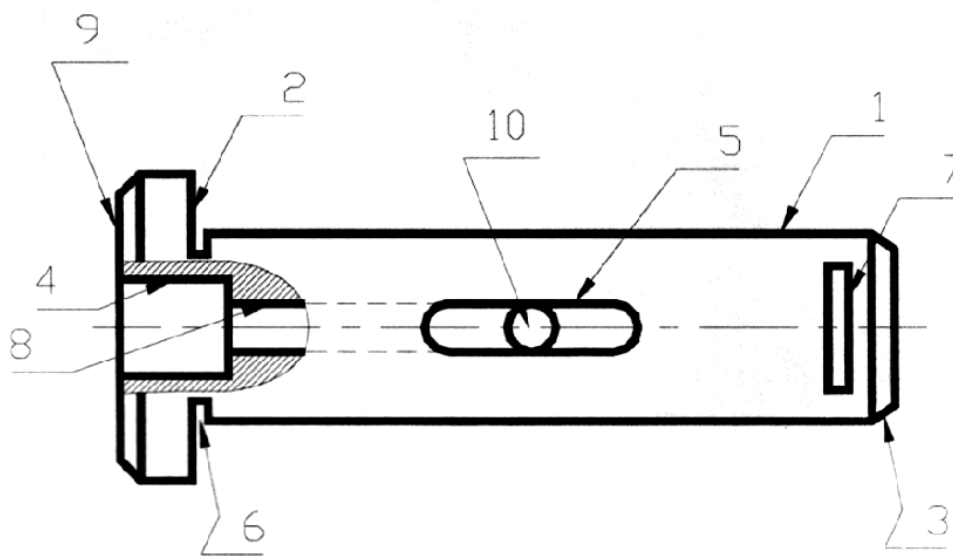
Ескіз деталі із номерами її поверхонь
